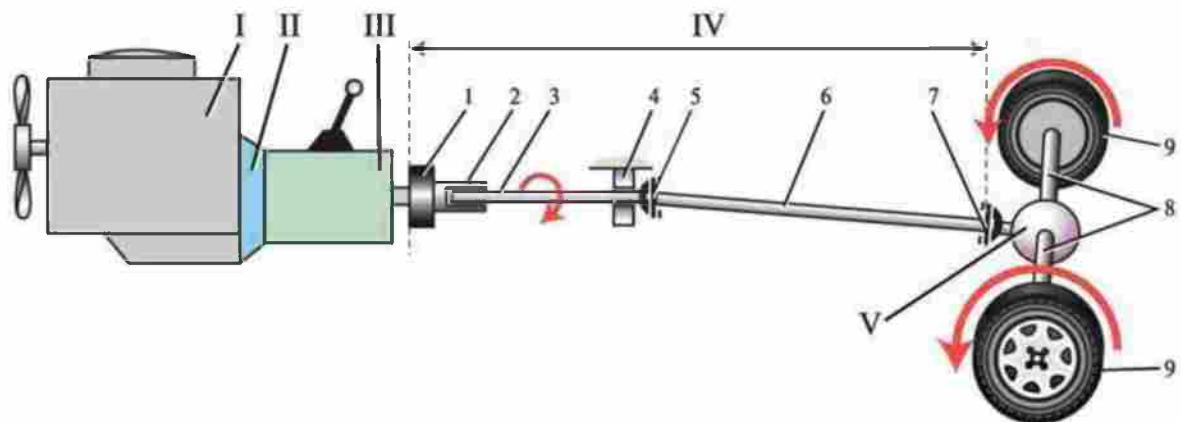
Схема трансмиссии заднеприводного автомобиля: I - Двигатель; II - Сцепление; III - Коробка передач; IV - Карданская передача: 1 - эластичная муфта; 2 - шлицевое соединение; 3 - передний карданный вал; 4 - подвесной подшипник; 5 - передний карданный шарнир; 6 - задний карданный вал; 7 - задний карданный шарнир; V - Задний мост с главной передачей и дифференциалом: 8 - полуоси; 9 - ведущие (задние) колеса Трансмиссия заднеприводного автомобиля включает в себя (рисунок 30): - сцепление, - коробку передач, - карданиную передачу, - главную передачу, - дифференциал, - полуоси. В автомобиле с приводом на передние колеса крутящий момент не уходит так далеко от двигателя, как в автомобиле с задним приводом. Все агрегаты трансмиссии переднеприводного автомобиля сконцентрированы под капотом машины и объединены в один большой агрегат.
